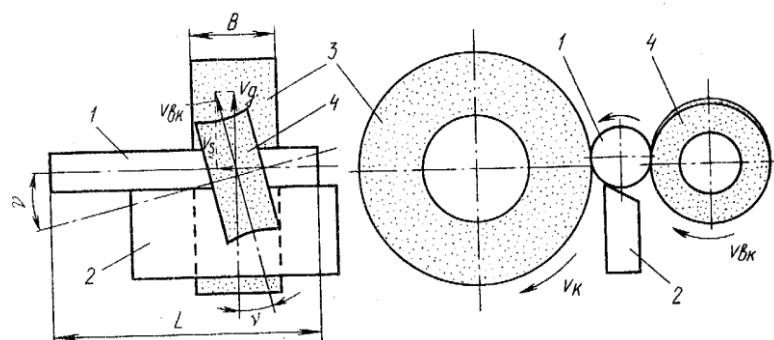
Схема безцентрового зовнішнього шліфування з повздовжньою подачею
